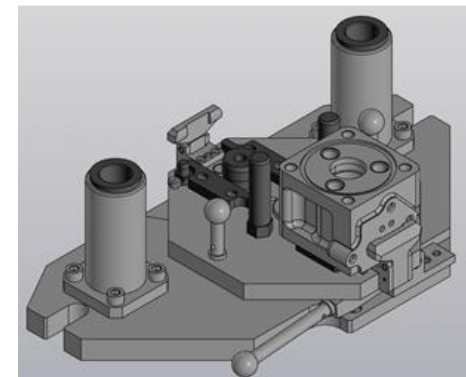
3D-модель приспособления для фрезерования впадин
